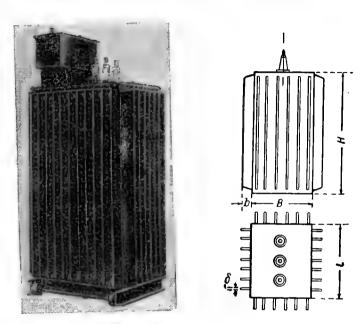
Форсированное охлаждение конденсатора с помощью приварки ребер к боковым стенкам корпуса.
